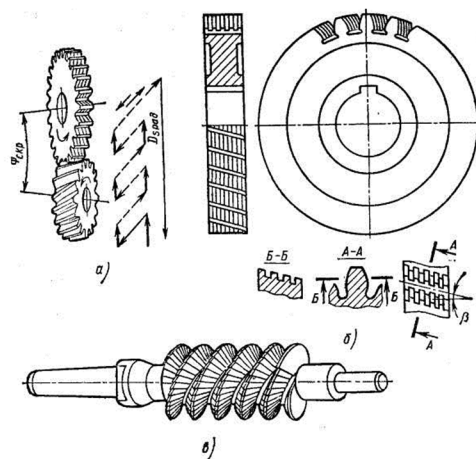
Схема зубошевингования и конструкция дискового и червячного шевера
